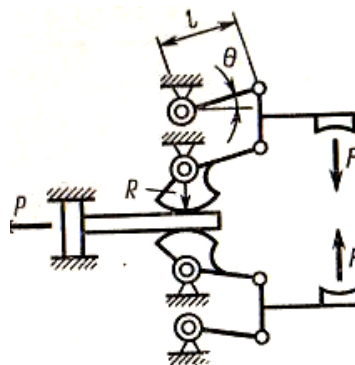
Кинематическая схема выбранного типа захватного устройства
